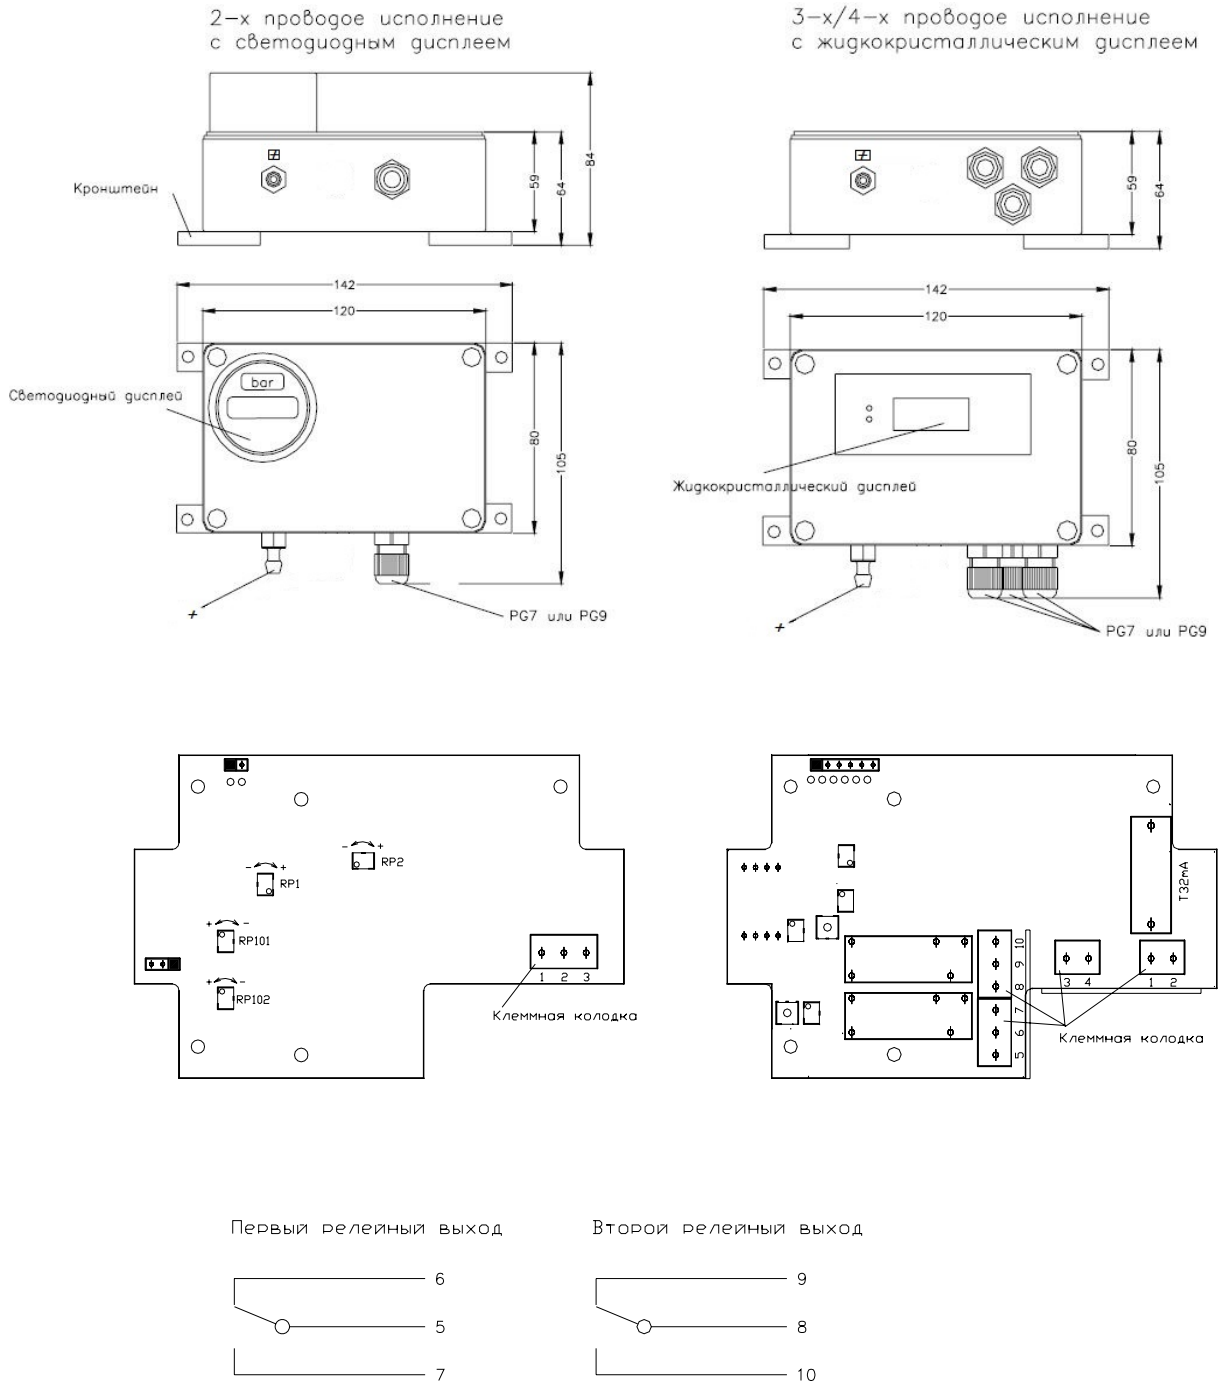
Габаритные размеры избыточного датчика DPS +
